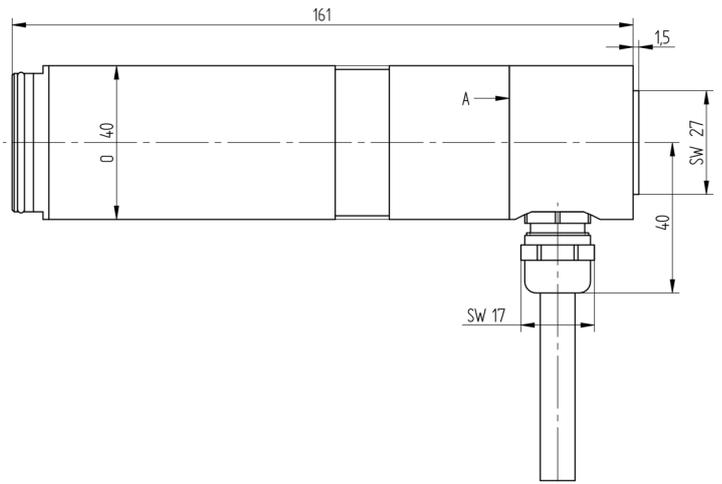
Maßzeichnung Flammfühler FFS07 Einsteckvariante
